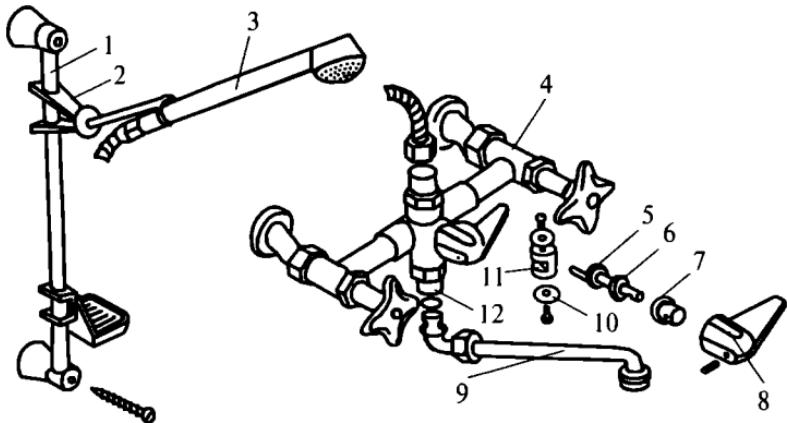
Смеситель с золотниковым переключателем, имеющим резиновые кольца и штангу: 1 — штанга; 2 — держатель; 3 — душевая сетка; 4 — корпус; 5 — кривошип; 6 — нитяное уплотнение; 7 — специальный винт; 8 — рукоятка; 9 — излив; 10 — прокладка золотника; 11 — золотник; 12 — переходник
